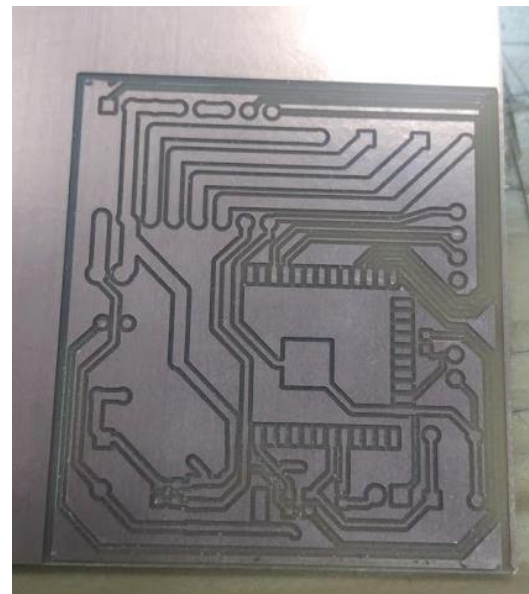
Exemple d'un PCB fabriqué avec un CNC
